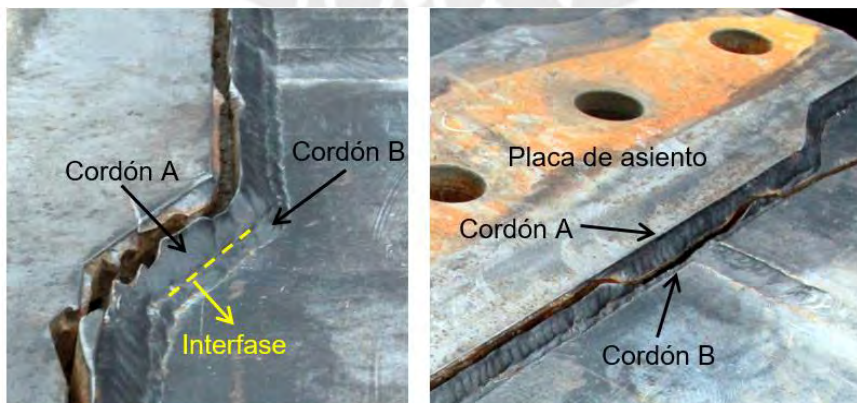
Imágenes de detalle del cordón de soldadura fisurado.
